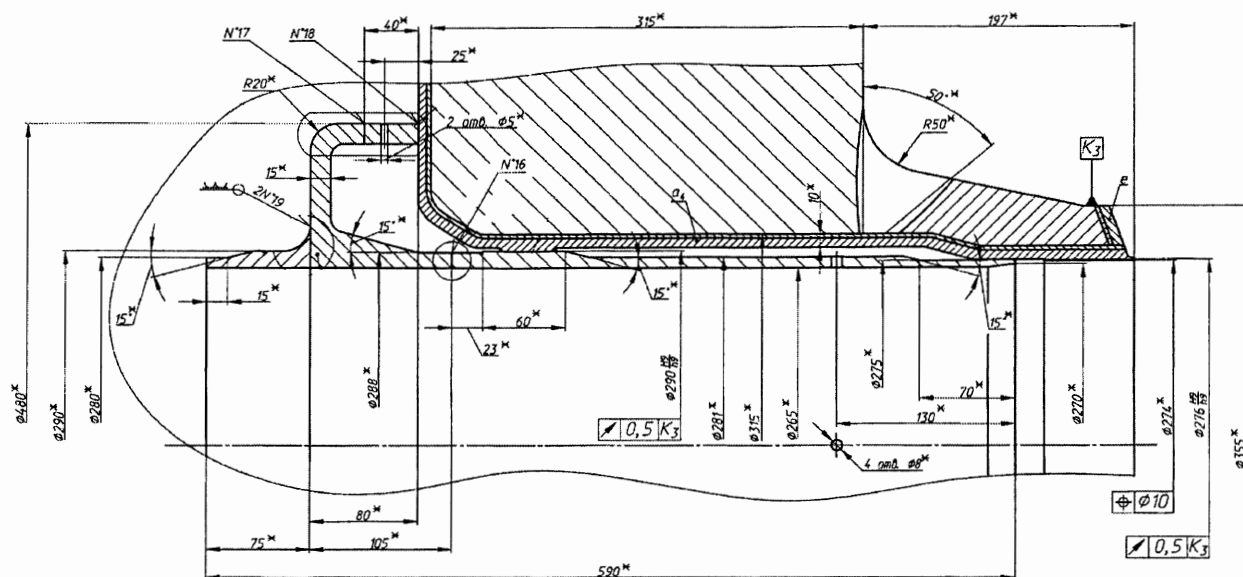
Разделка кромок под сварку патрубков САОЗ
